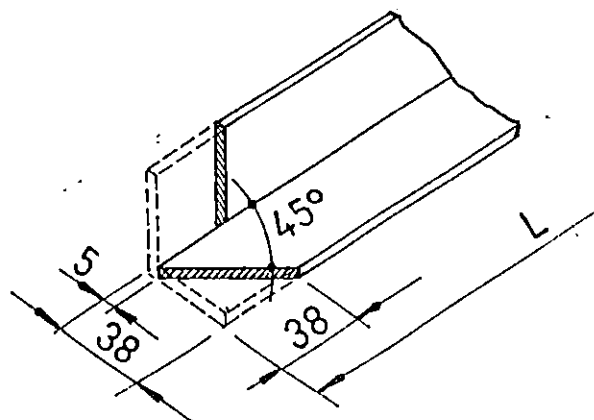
Corte a 45° en extremos piezas para marco intermedio.
